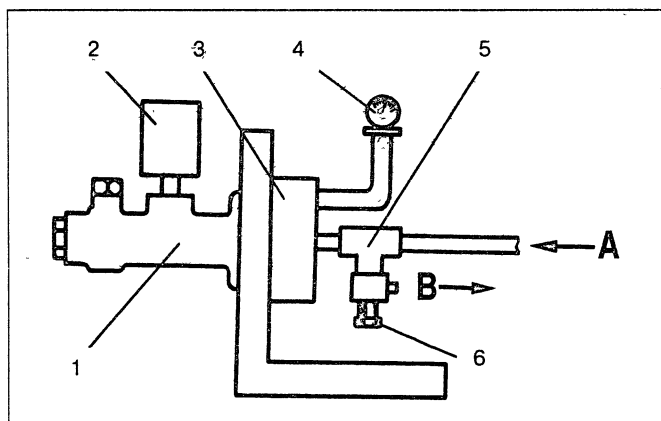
Проверка герметичности заднего уплотнительного кольца: 1 – главный цилиндр; 2 – сосуд; 3 – переходник с уплотнителем; 4 – манометр; 5 – тройник; 6 – регулировочный винт; A – воздух от компрессора; B – выпуск воздуха
